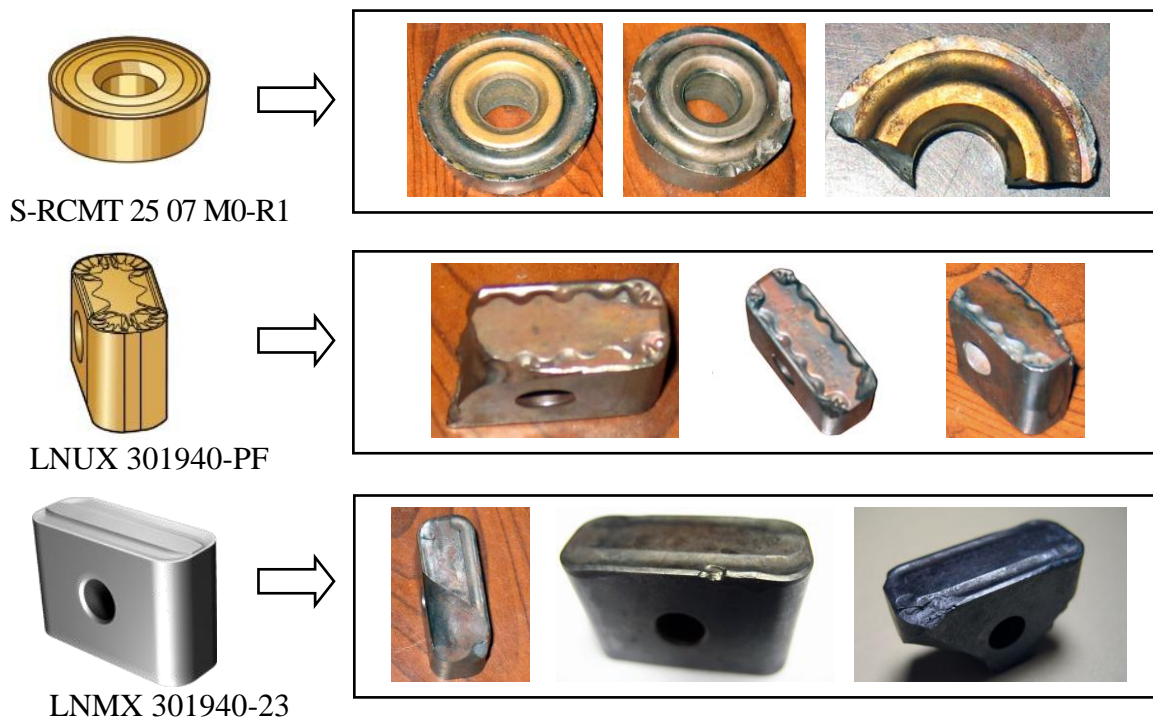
Види зношування твердосплавних пластин при обробці на копіювальному колесотокарному верстаті
